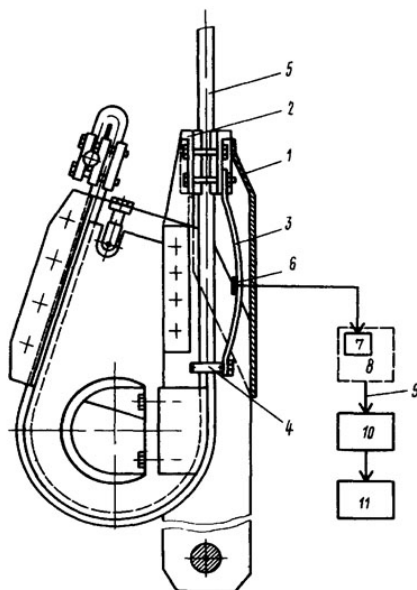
Устройство для контроля натяжения тягового органа подъемной установки
